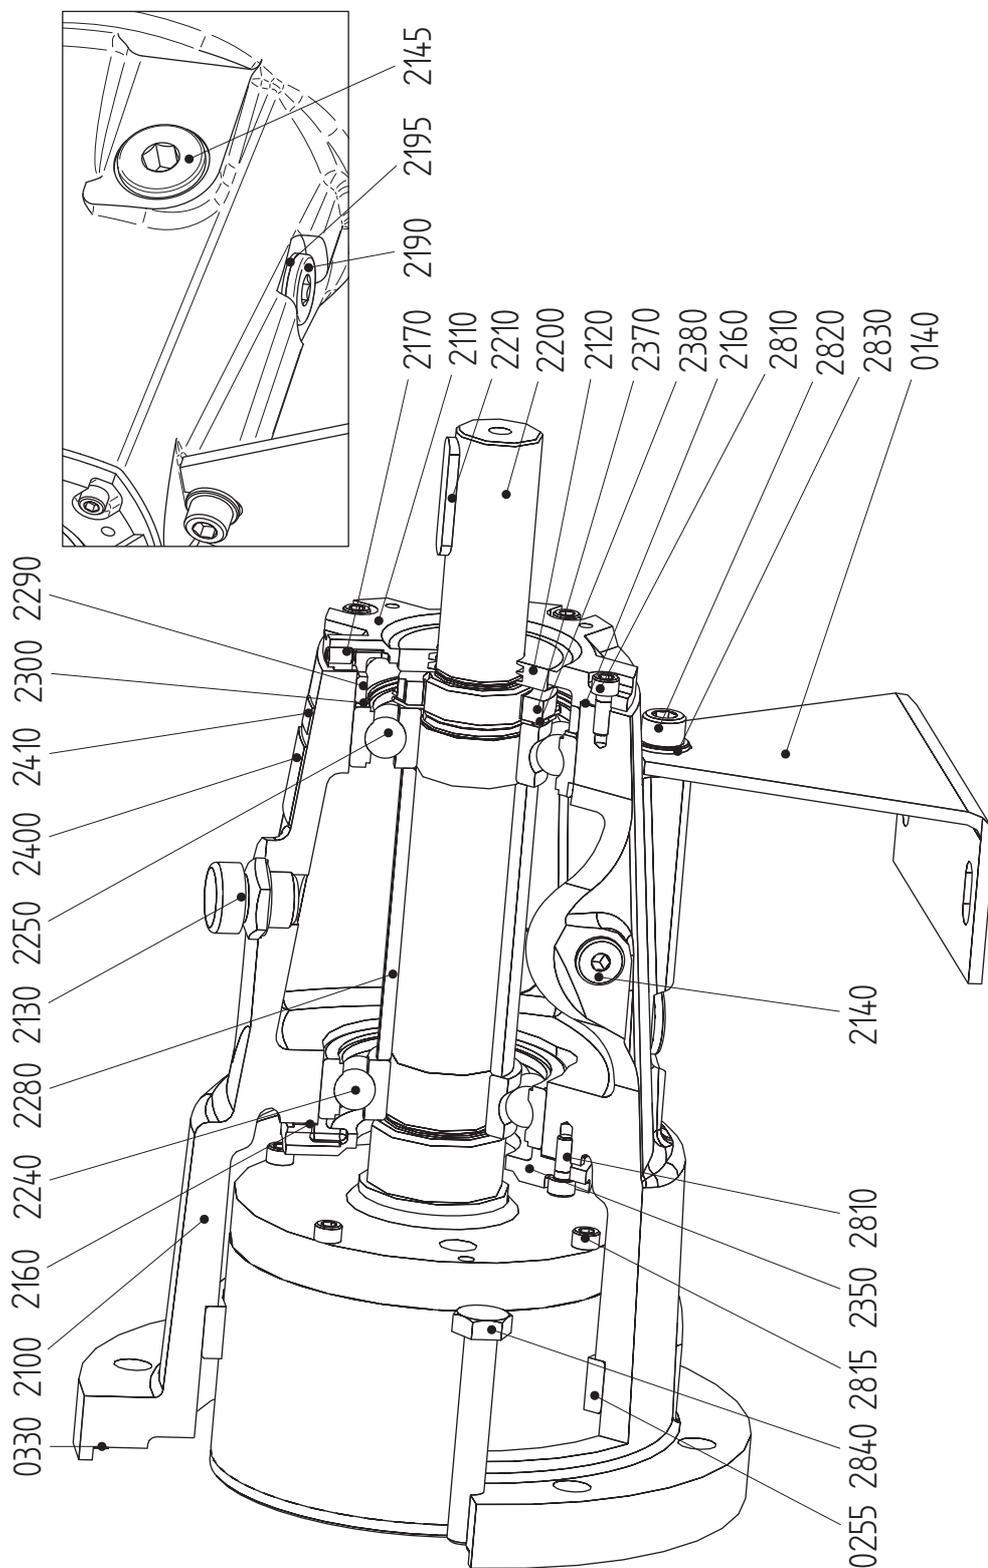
Роликовый подшипник L1 с консистентной смазкой
